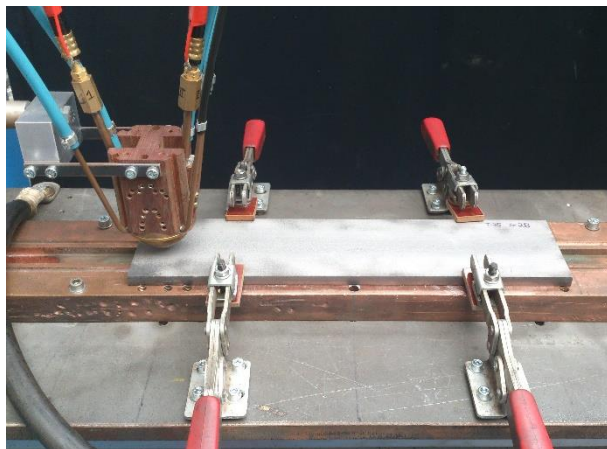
Corpo de prova posicionado para ensaio de soldagem tipo cordão sobre chapa
